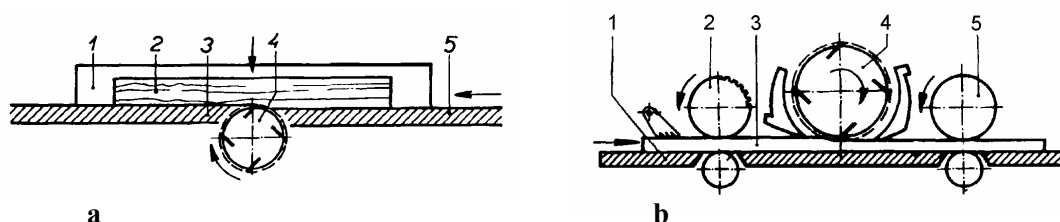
Opracovanie prírezu (obrobku) v pozdĺžnom smere
